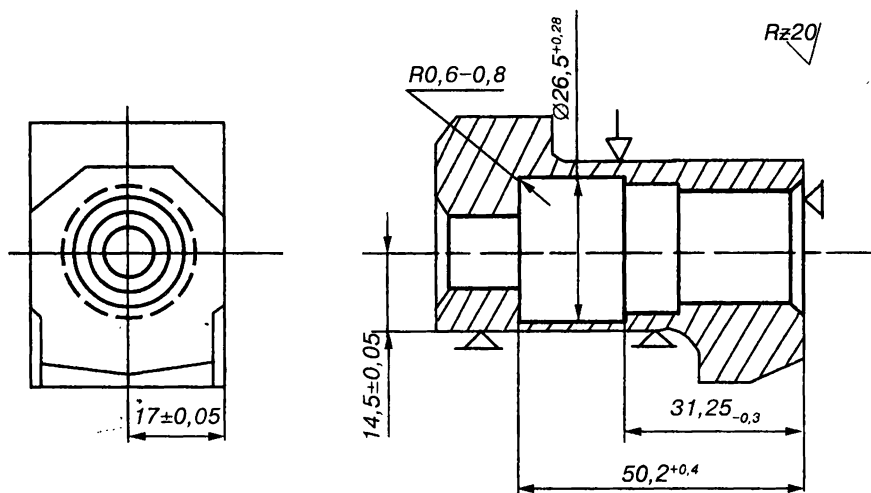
Фрезерование котла на станке модели 716ИФ
